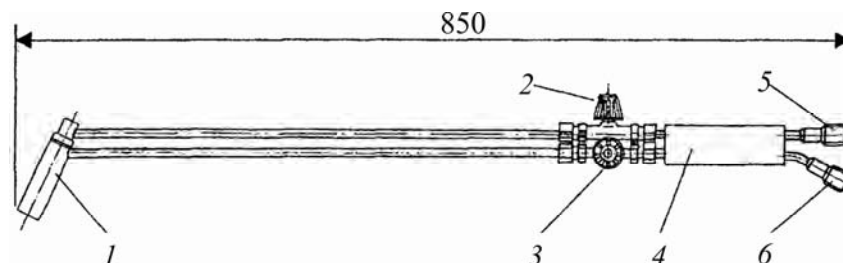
Горелка ПВ-1: 1 — головка горелки; 2 — вентиль подачи воздуха; 3 — вентиль подачи горючего; 4 — державка; 5 — штуцер воздуха М 16 × 1,5; 6 — штуцер горючего М 16 × 1,5 Н
